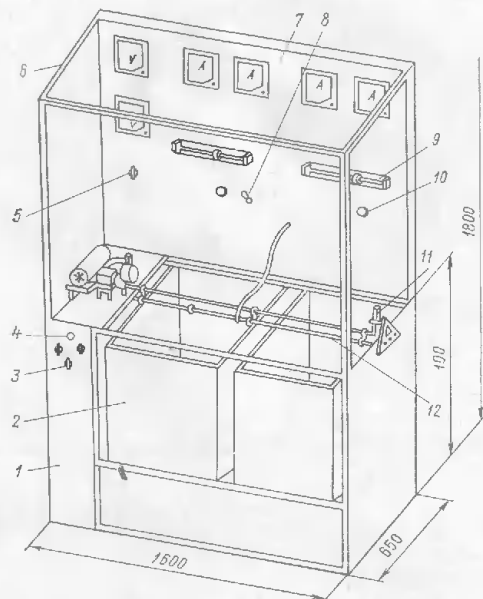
Схема установки для изготовления формообразующих деталей пресс-форм:
